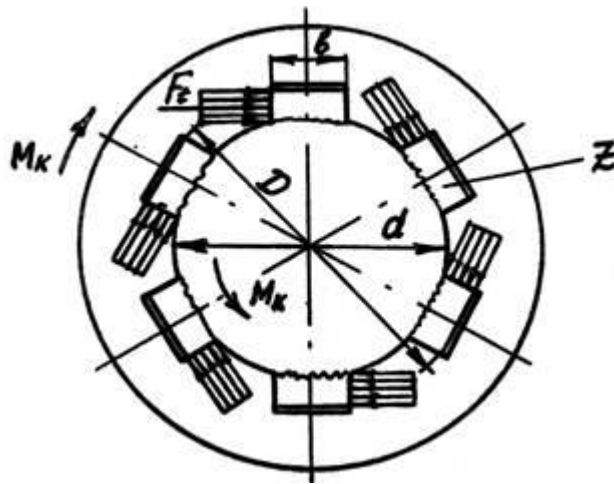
Розрахункова схема шліцевого з'єднання
